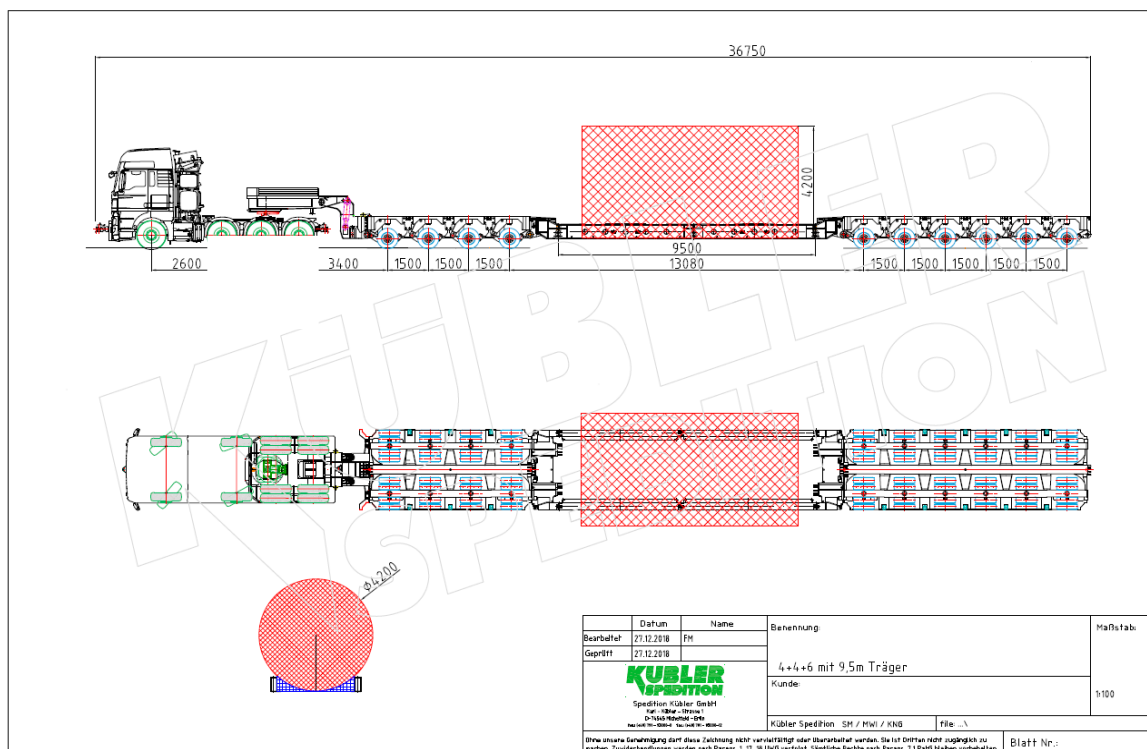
Kesselbrücke (beispielhaft Fa. Kübler)
